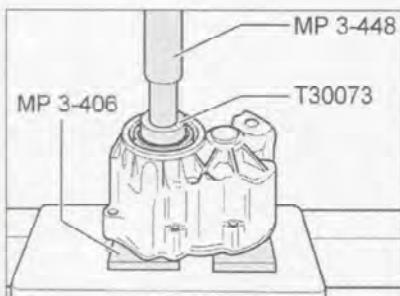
Извлечение заднего подшипника первичного вала.
